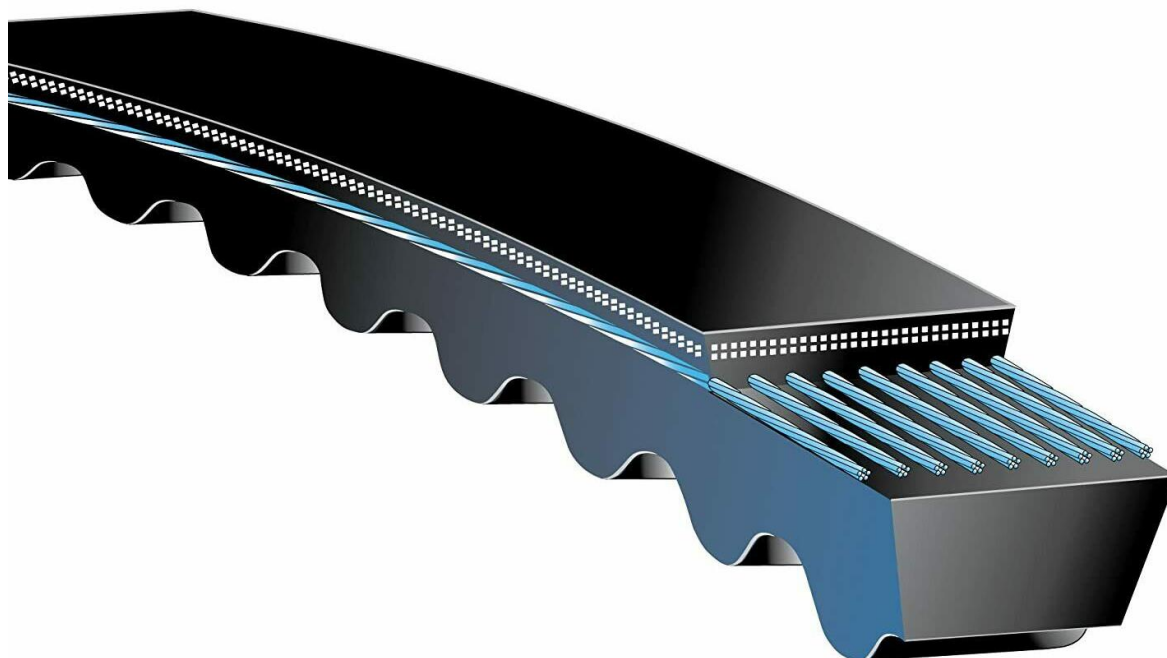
Общий вид нормального клинового ремня с зубчатой внутренней поверхностью
